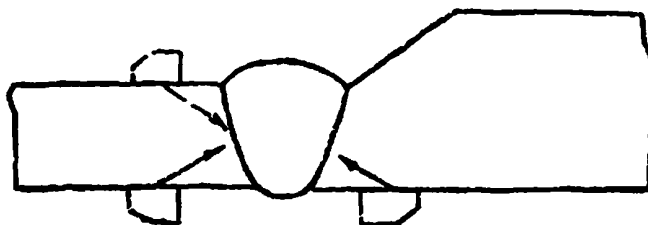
Пример контроля сварных соединений листов, имеющих скосы от кромок
